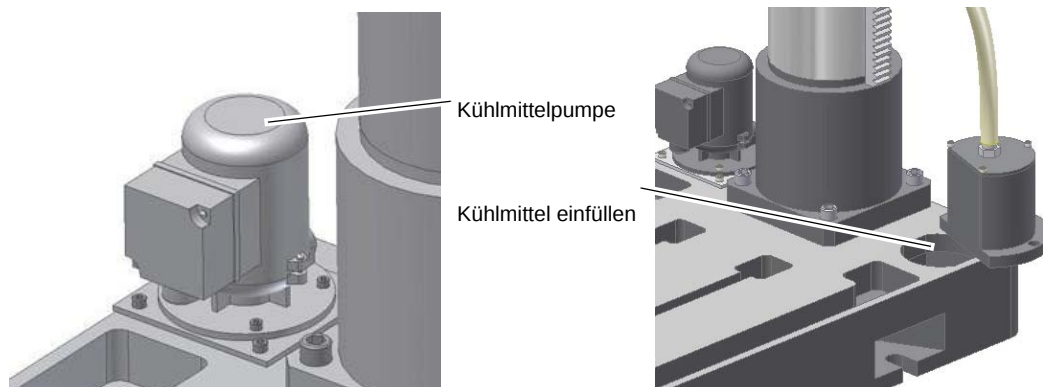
Kühlmittelpumpe, Kühlmittel Einfüllöffnung
